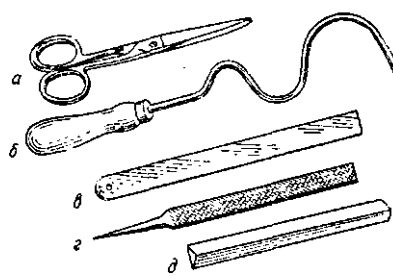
Режущий инструмент для стеклодувных работ. а — ножницы; б — крючок; в — нож; г- напильник; д — призма.
